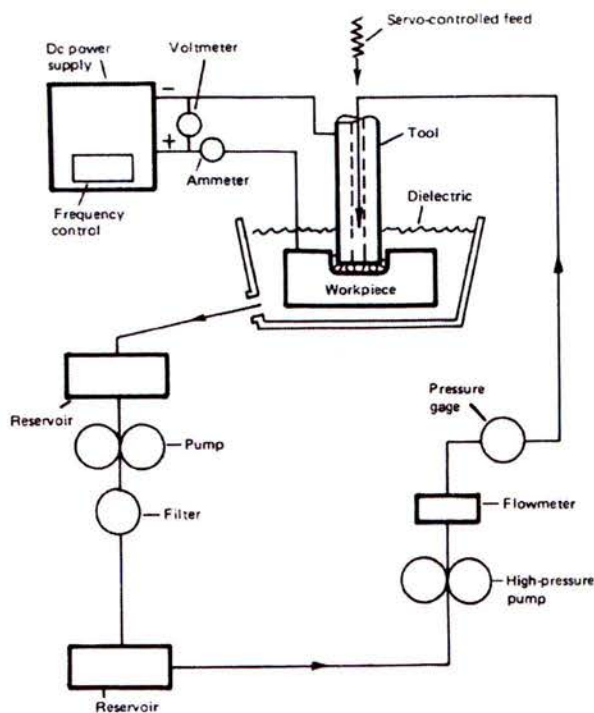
Esquema construtivo de uma máquina de EDM diesinking
